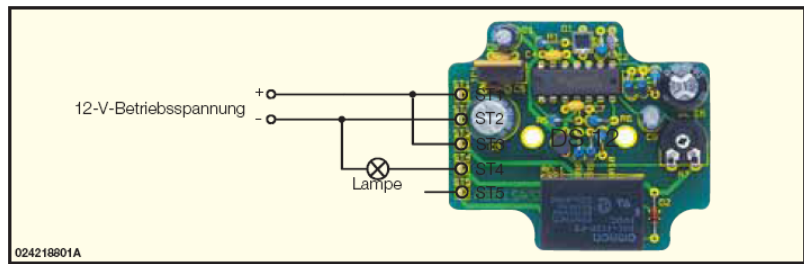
Beispielkonfiguration mit dem Dämmerungsschalter
